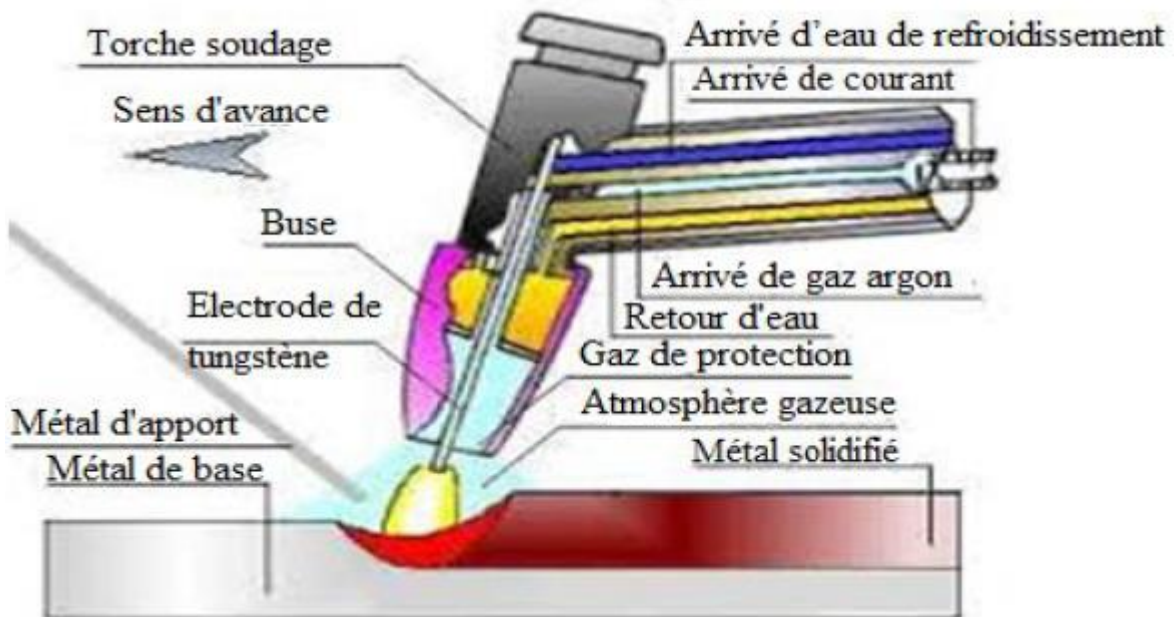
Procédé de soudage TIG (avec sa torche) [
